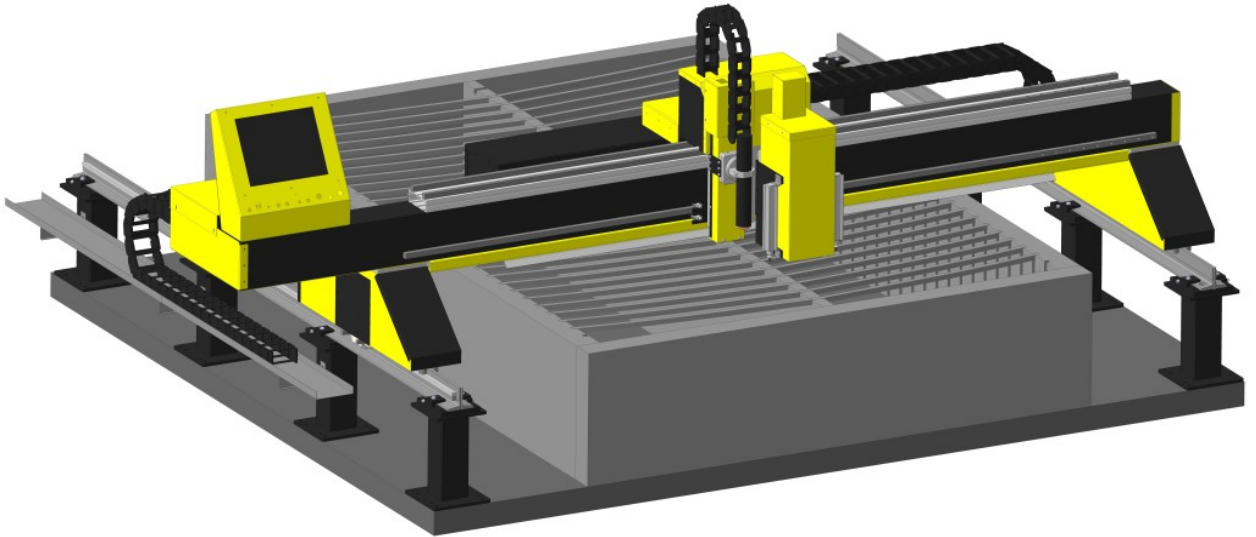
Установка для термічного різання S-CUT 3
